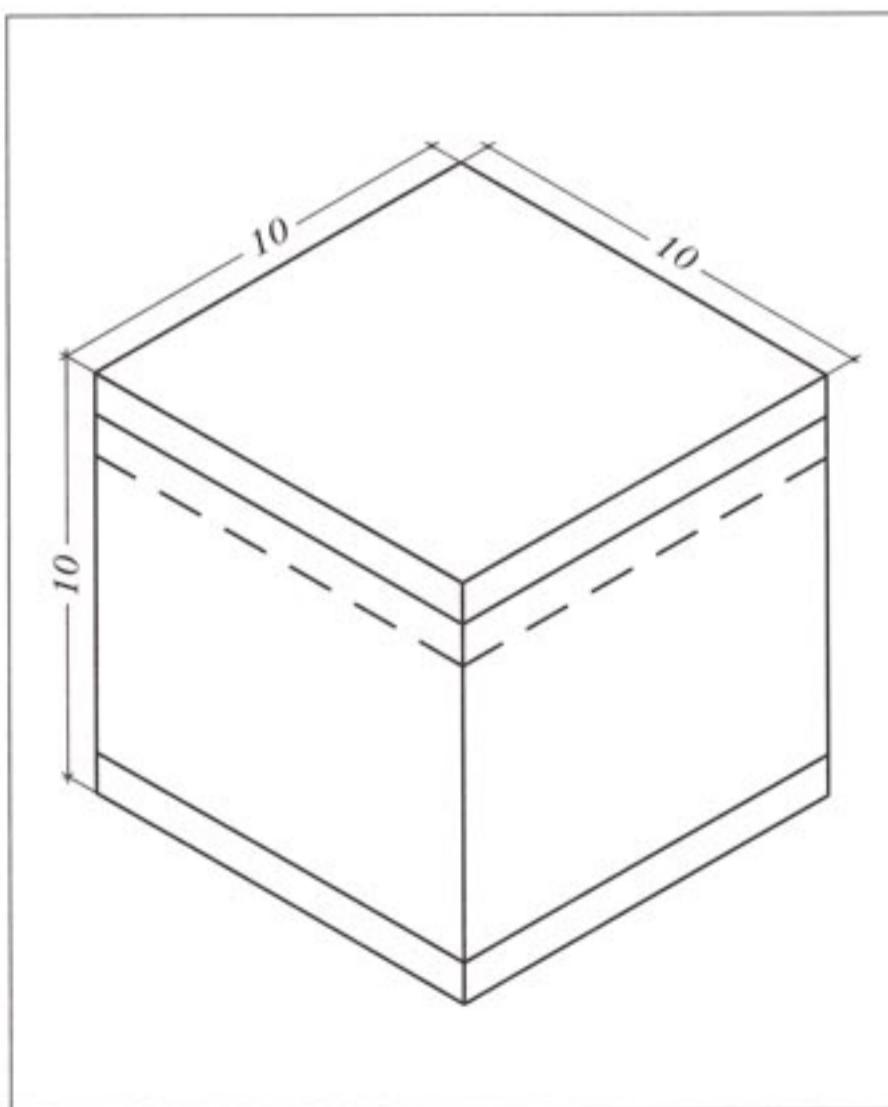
Общий вид заготовки. Пунктирной линией показано место отделения боковин крышки
